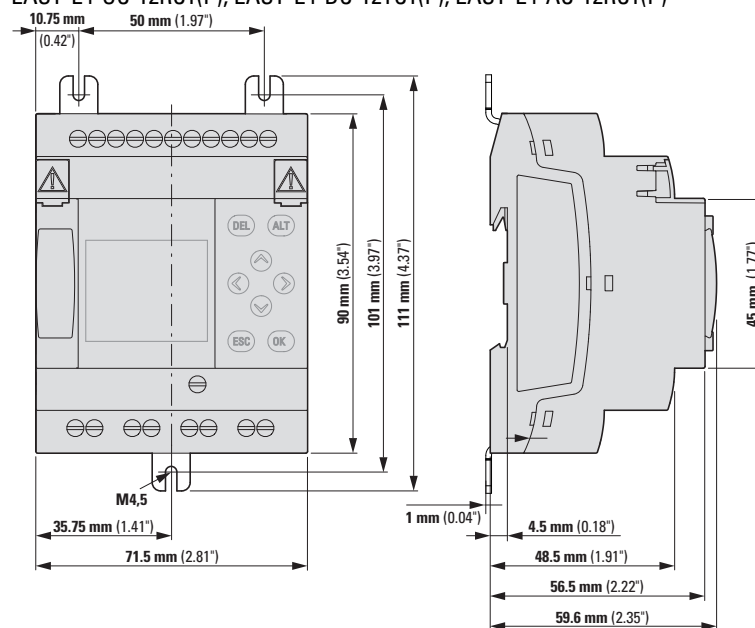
Dimensions en mm (pouces) appareils de base EASY-E4-...-12...C1(P)
